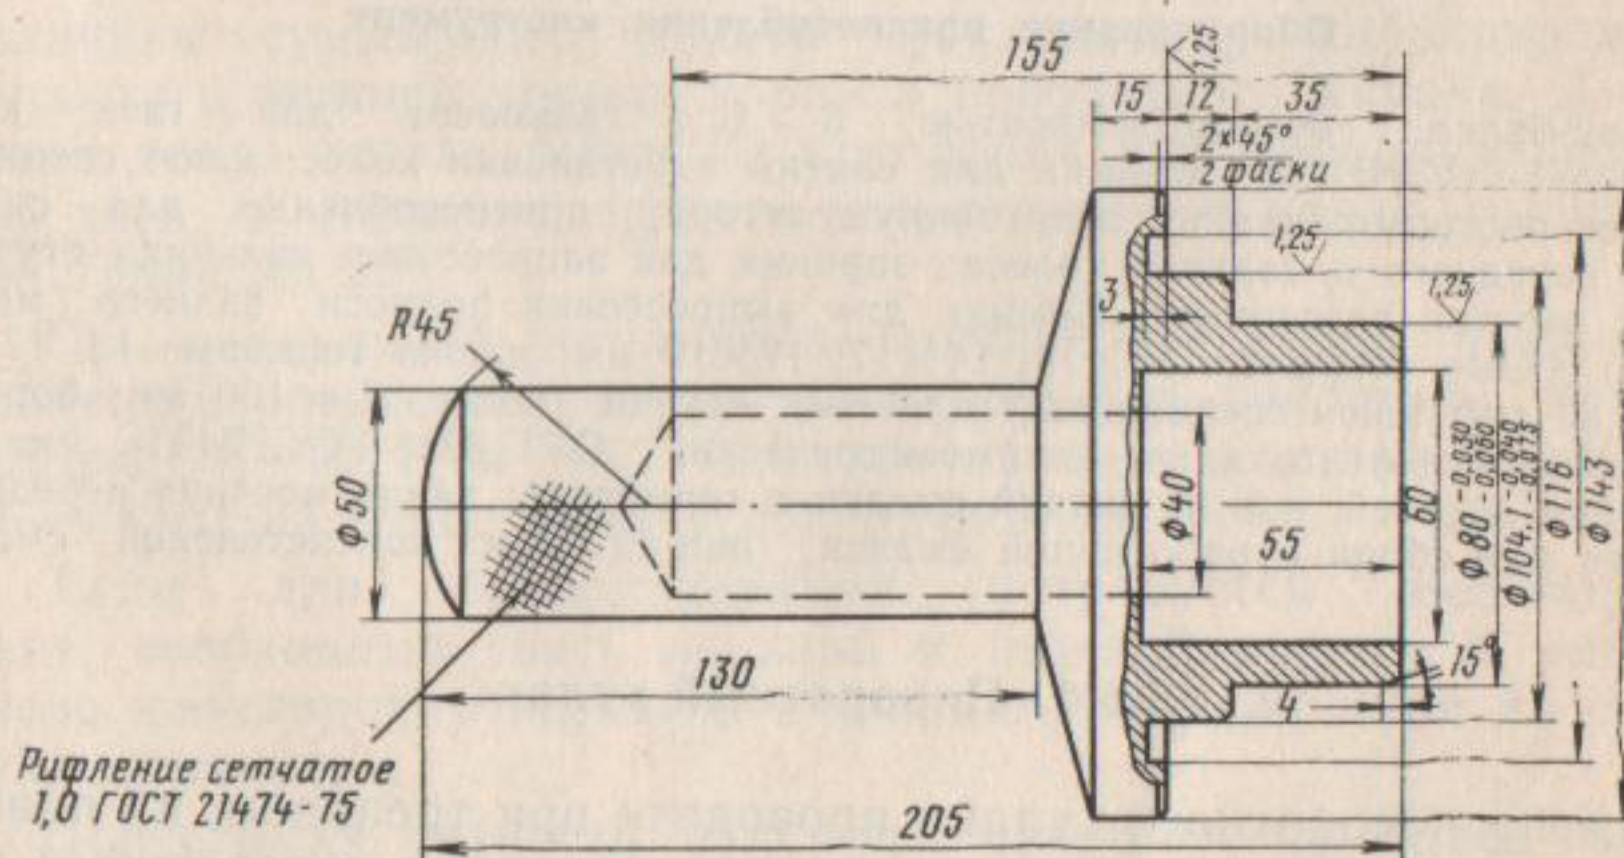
Оправка для запрессовки сальника ступицы колеса
